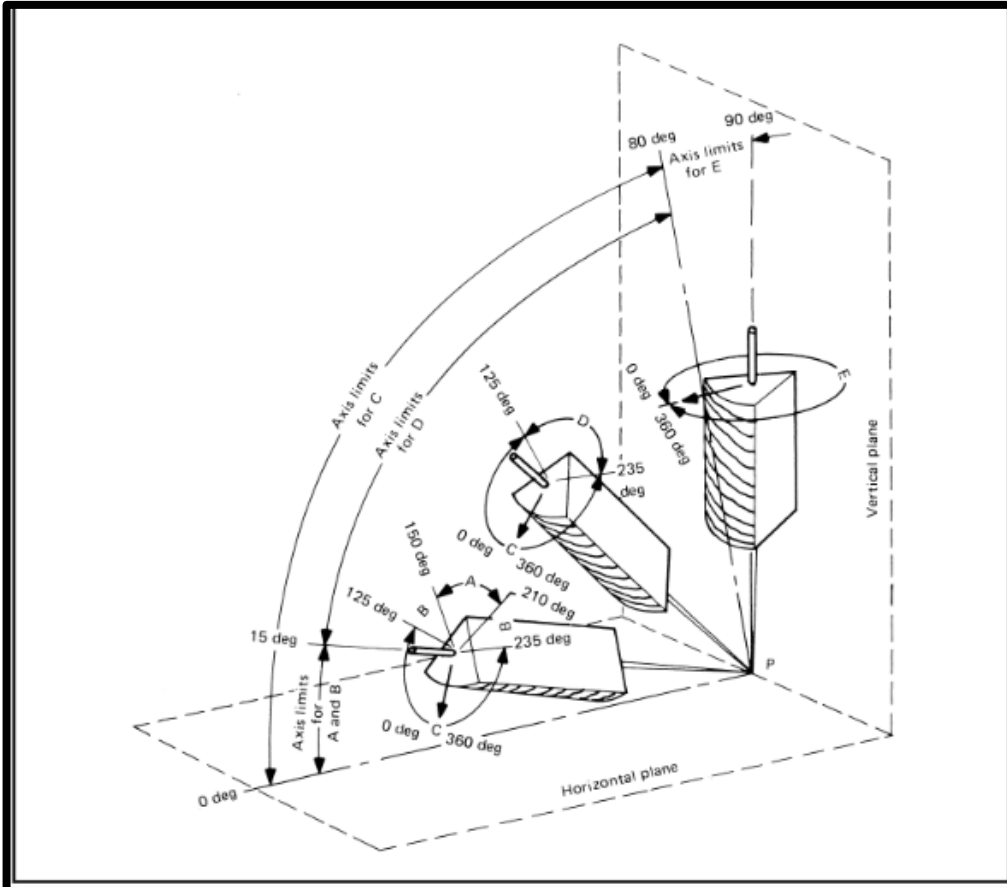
La rotación de la cara de una línea perpendicular al eje de soldadura. Tomada del estándar ASME sección IX
